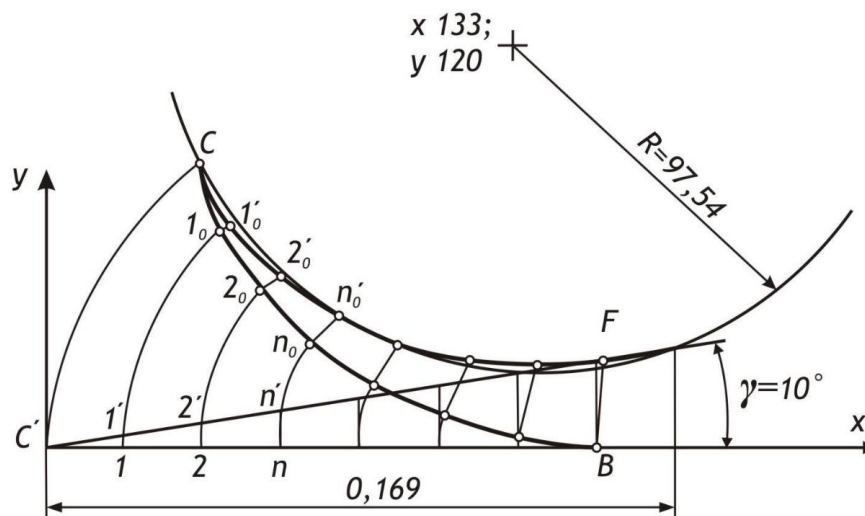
Схема формування криволінійної напрямної поверхні ножа CF за траєкторією руху СВ.
